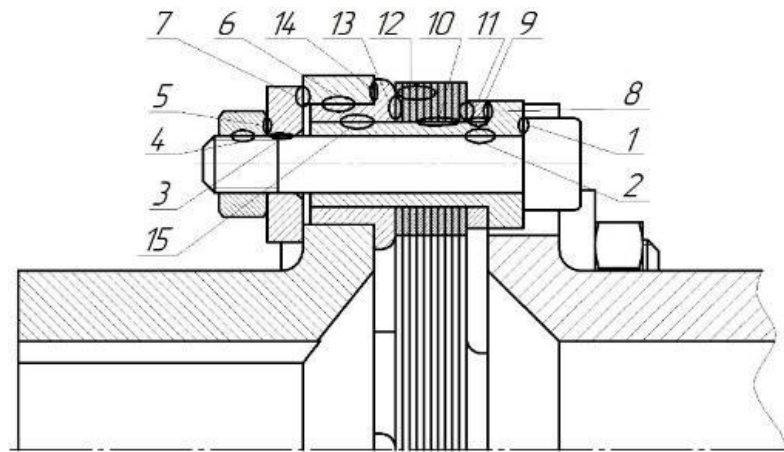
Контактуючі поверхні ПМ, що піддаються Ф-К: втулка і головка болта; – втулка і шийка болта; – шайба і шийка болта; – різьба болта і гайки; – шайба і гайка; – напівмуфта і п'ята; – напівмуфта і шайба; – мала шайба і головка втулки; – мала шайба і шийка втулки; – ГЕ і шийка втулки; – ГЕ і мала шайба; – ГЕ і ГЕ; – ГЕ і п'ята; – напівмуфта і п'ята; – втулка і п'ята [140].
